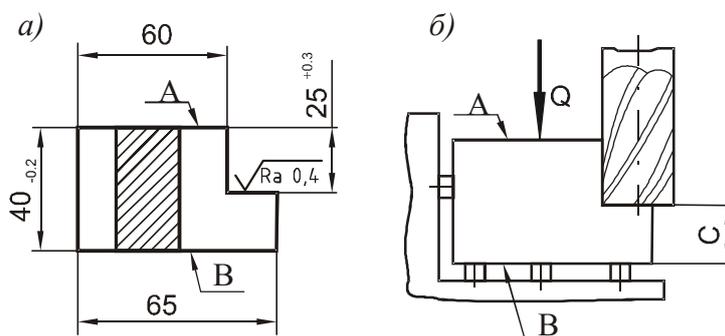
Схемы фрезерования уступа при различных вариантах установки заготовки: а – операционный чертеж заготовки; б – схема установки заготовки при несовпадении измерительной А и установочной В баз; Q – зажимная сила
